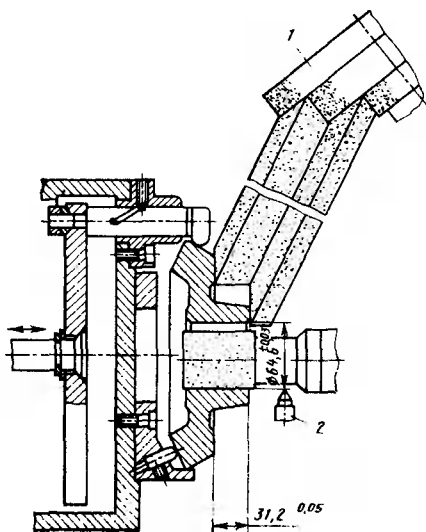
Схема шлифования базовых поверхностей конического колеса со ступицей
